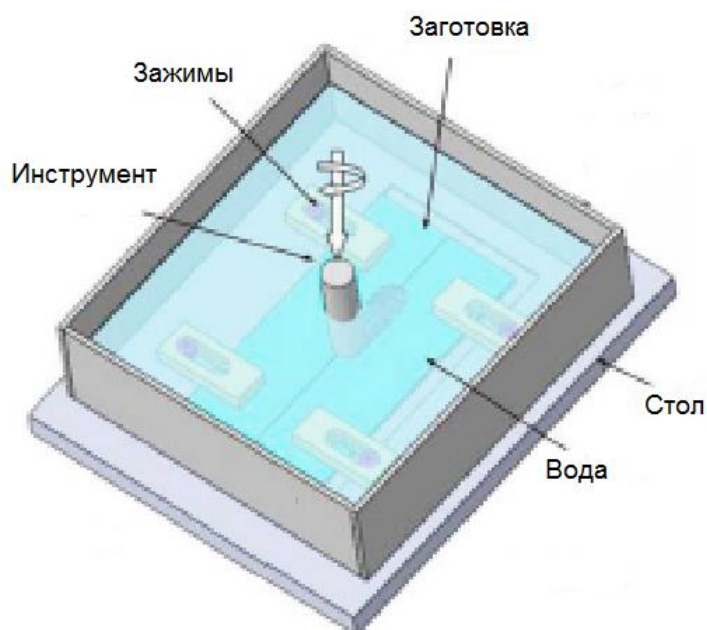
Сварка трением с перемешиванием под водой
